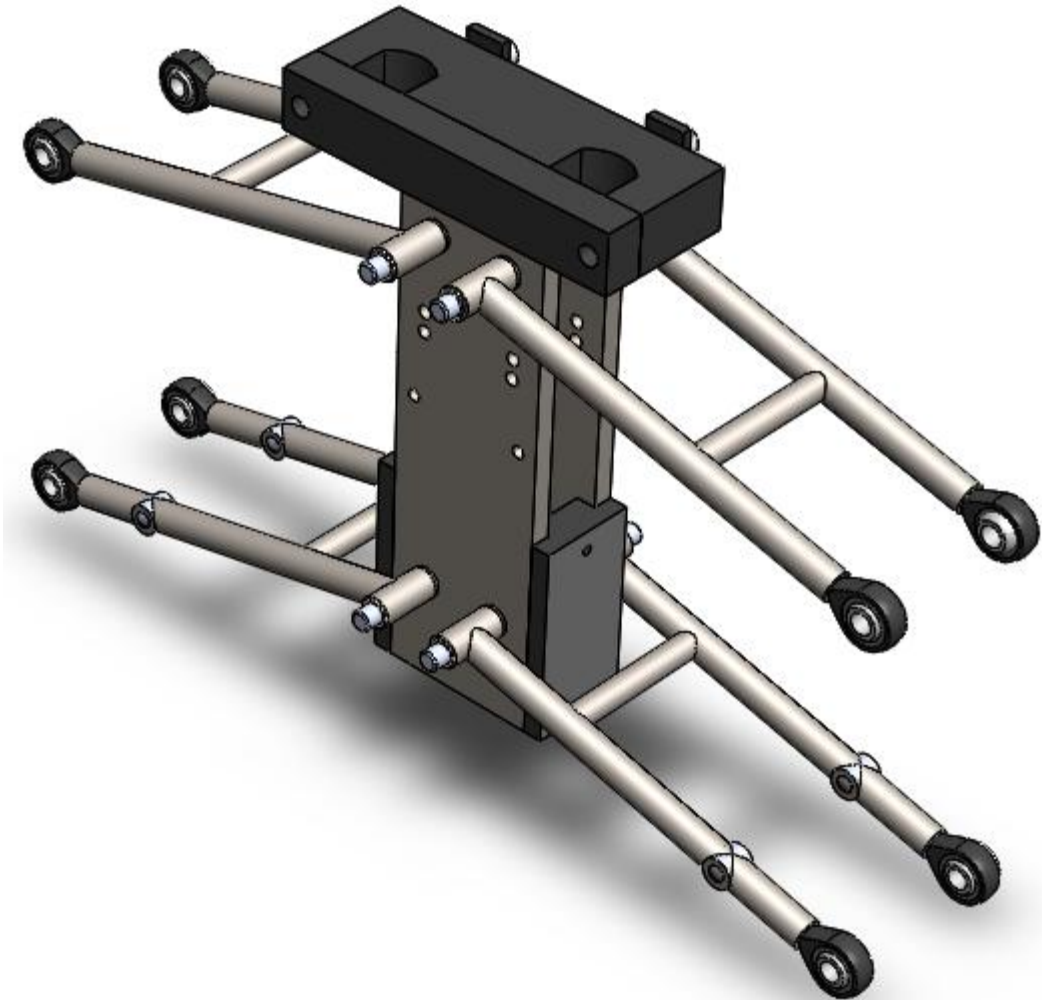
Vue 3D de l'assemblage Barre de suspension et axe sur châssis
